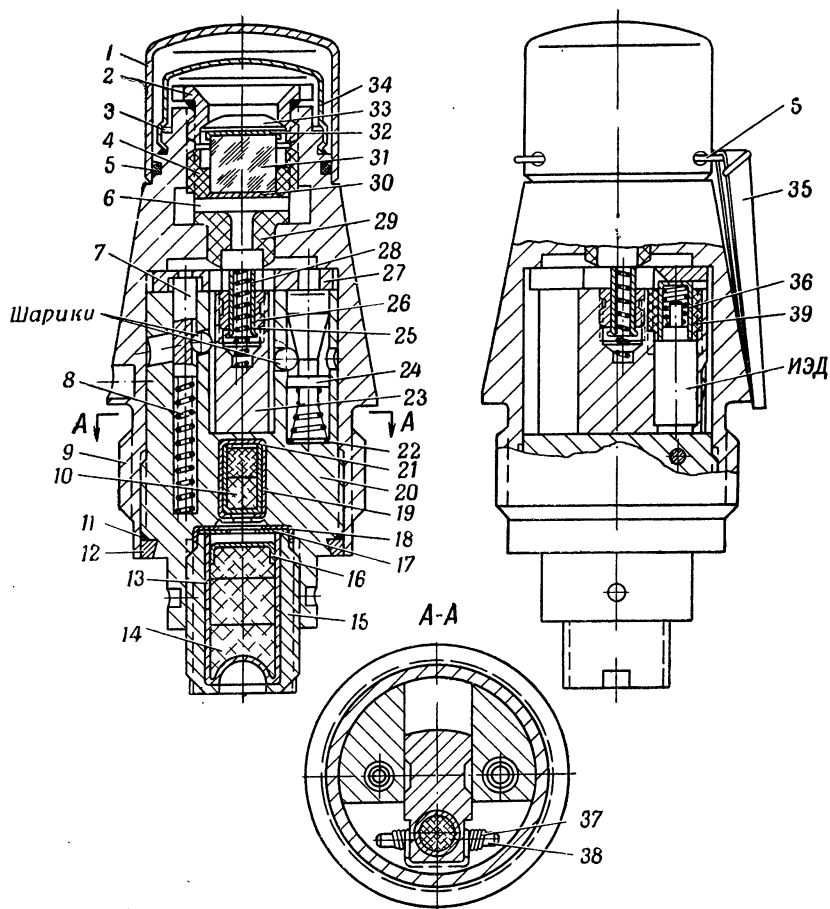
Взрыватель ГПВ-2 (положение деталей до выстрела):
